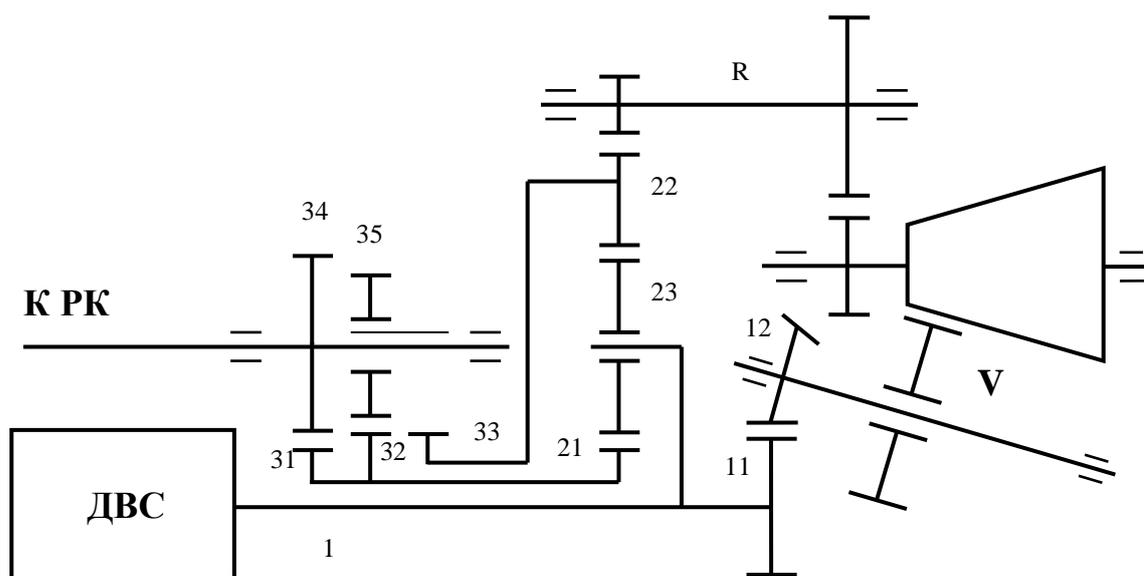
Кинематическая схема трансмиссии с зубчатым вариатором:
